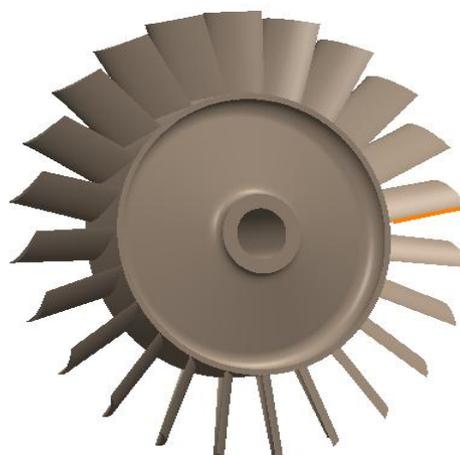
Turbina axial dimensionada e desenhada em ferramenta CAD
